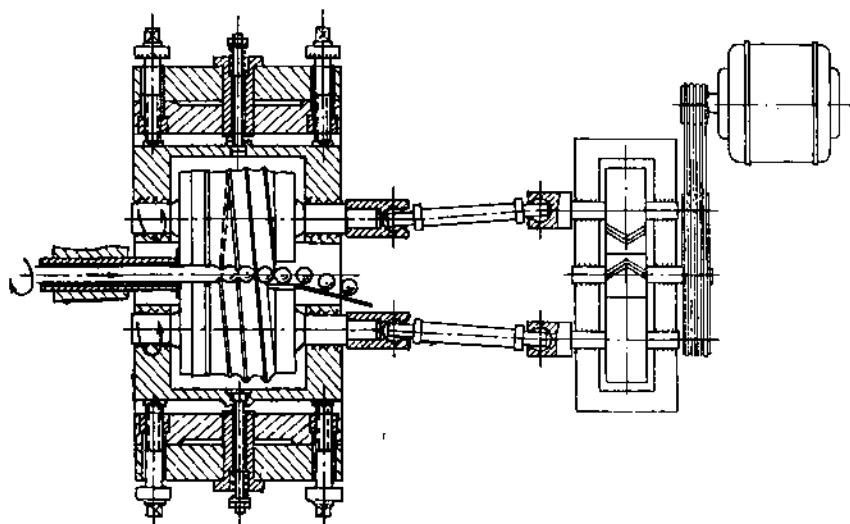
Кинематическая схема стана для прокатки шаров конструкции ЦНИИТмаша
